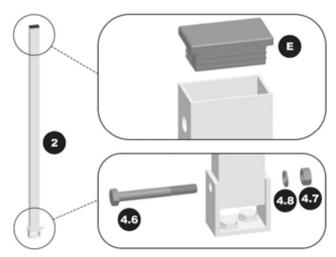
Trägerrohr (2) mit Sechskantschraube (3.6/4.6), Federring (3.7/4.8) und Sechskantmutter (3.8/4.9) an den hinteren U-Stücken (3.1/4.1) befestigen.
